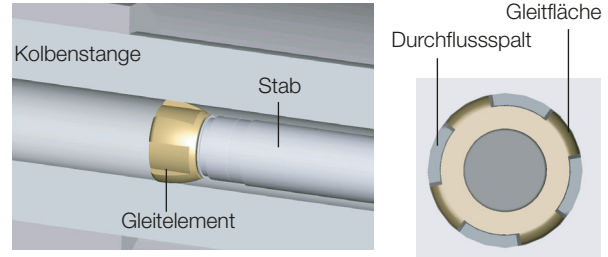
Detailansicht und Draufsicht Gleitelement
